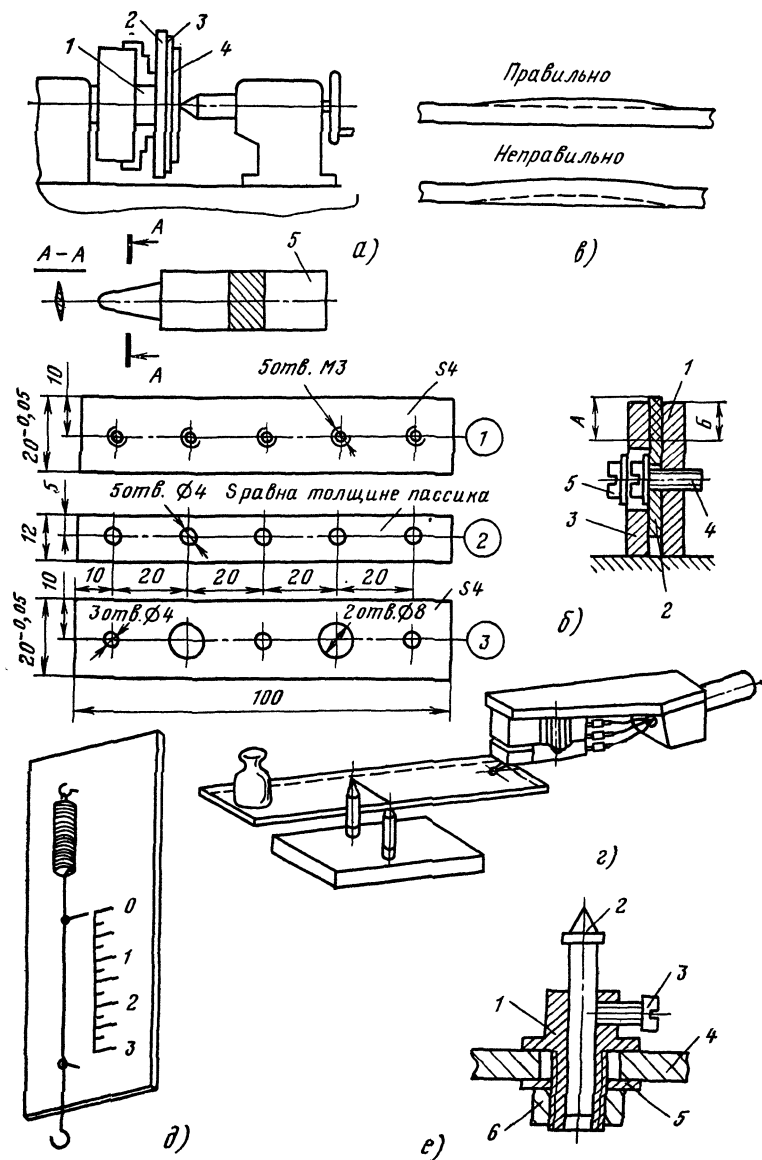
Приспособления для изготовления и регулировки проигрывателя.
